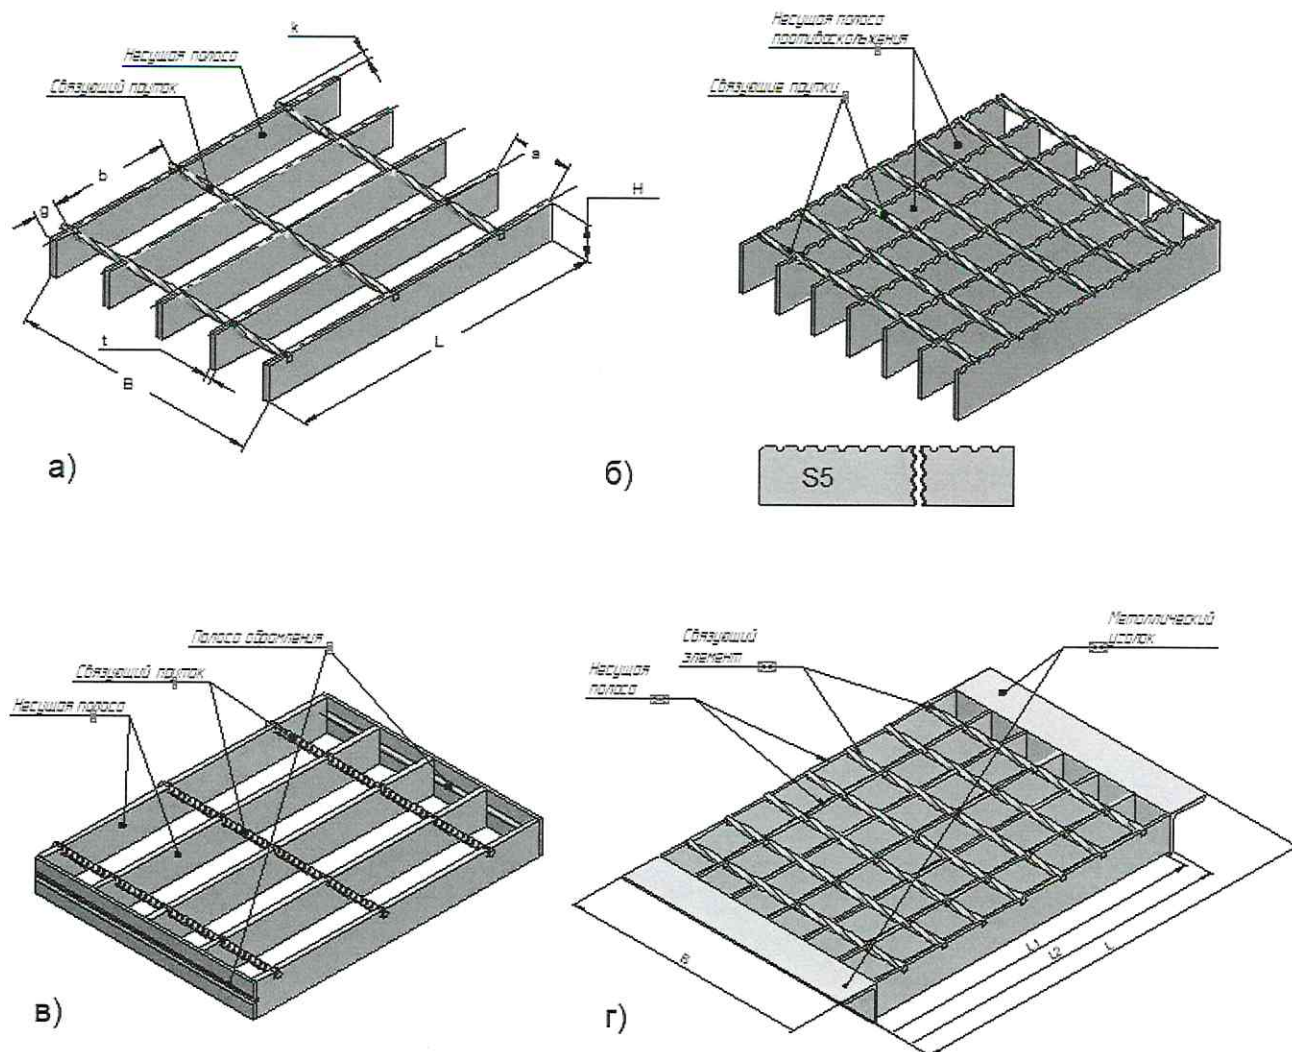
Типовой вид сварного настила: а) без обрамления со стандартной несущей полосой; б) без обрамления с полосой противоскольжения; в) с полосой обрамления; г) с уголком обрамления.
